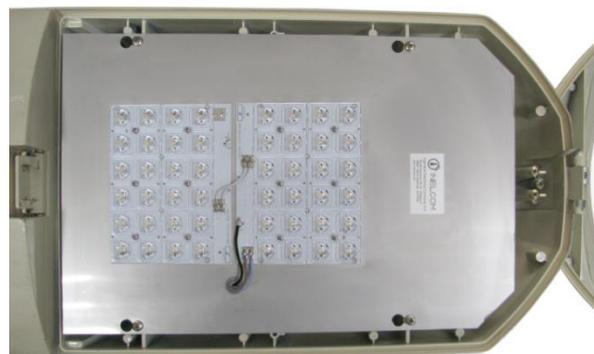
Montaje del Módulo óptico ILUZ251.Q
